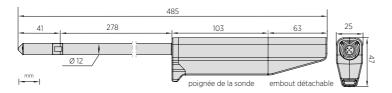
Dimensions de la sonde HMP80L, vue de côté et de dessous
